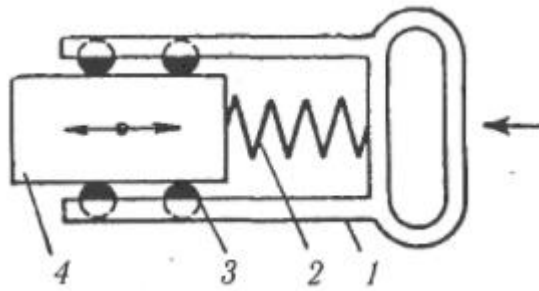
Віброізований держак: 1 – держак; 2 – пружина; 3 – підшипник; 4 – корпус [28]
